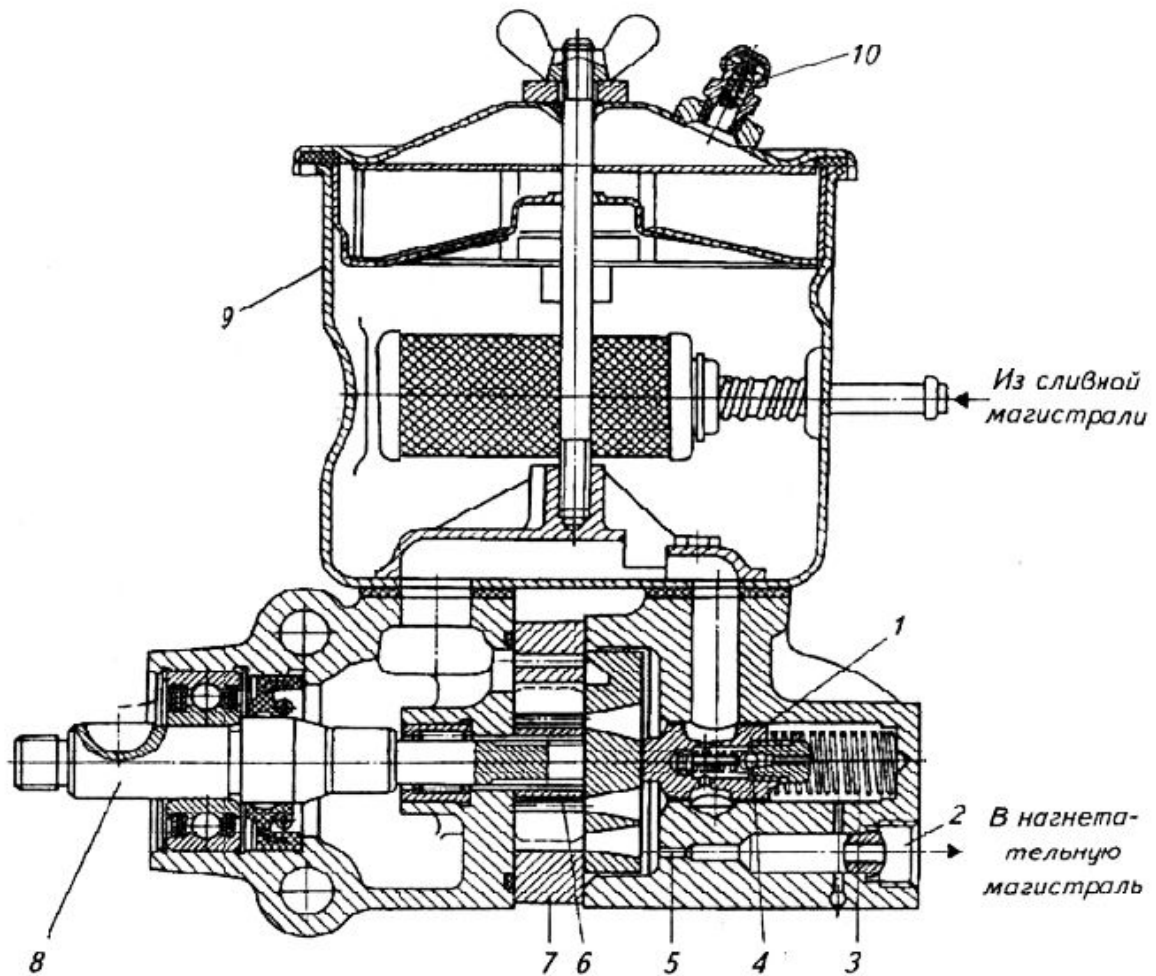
Пластинчатый насос гидроусилителя рулевого управления
